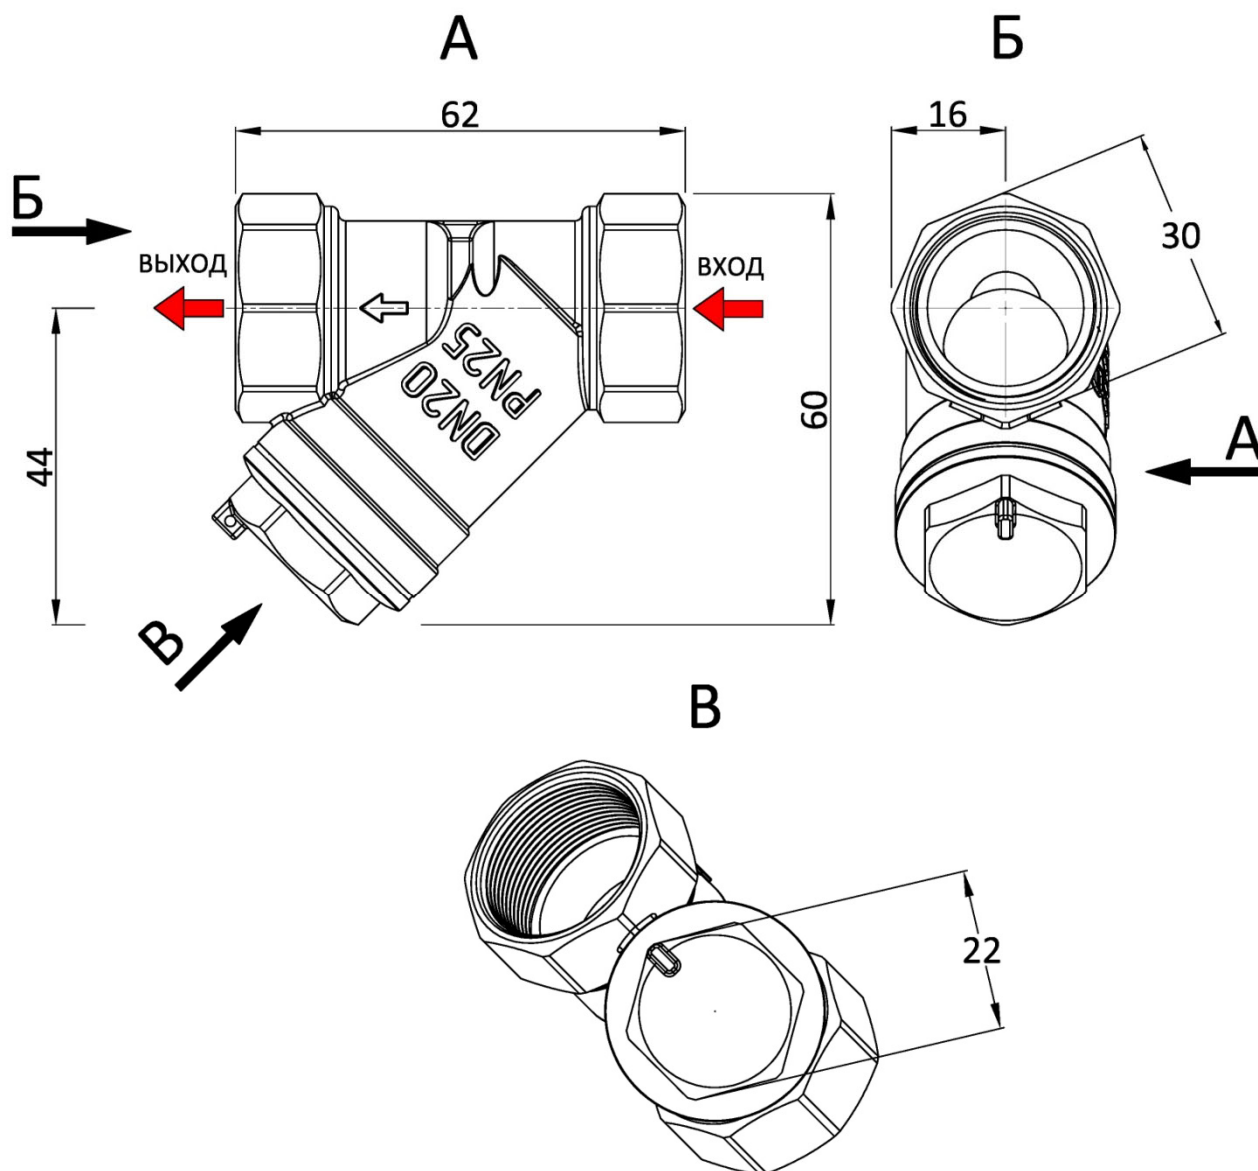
Габаритные размеры фильтра газового «РЕД-20-Н-Р»,
